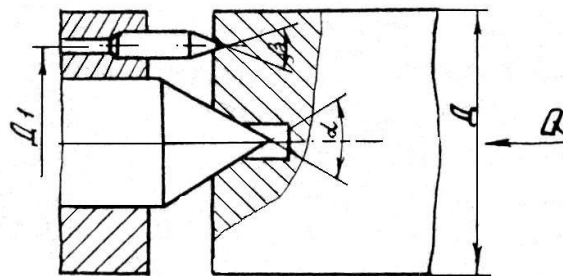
Розрахункова схема установки заготовки в плаваючих центрах з повідковим улаштуванням
